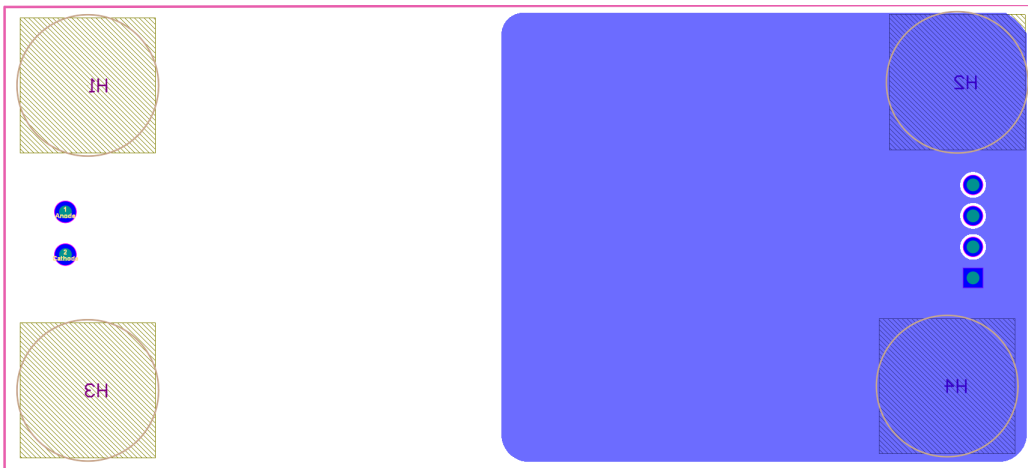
ISOM8110DFGEVM PCB 布局 - 底层
